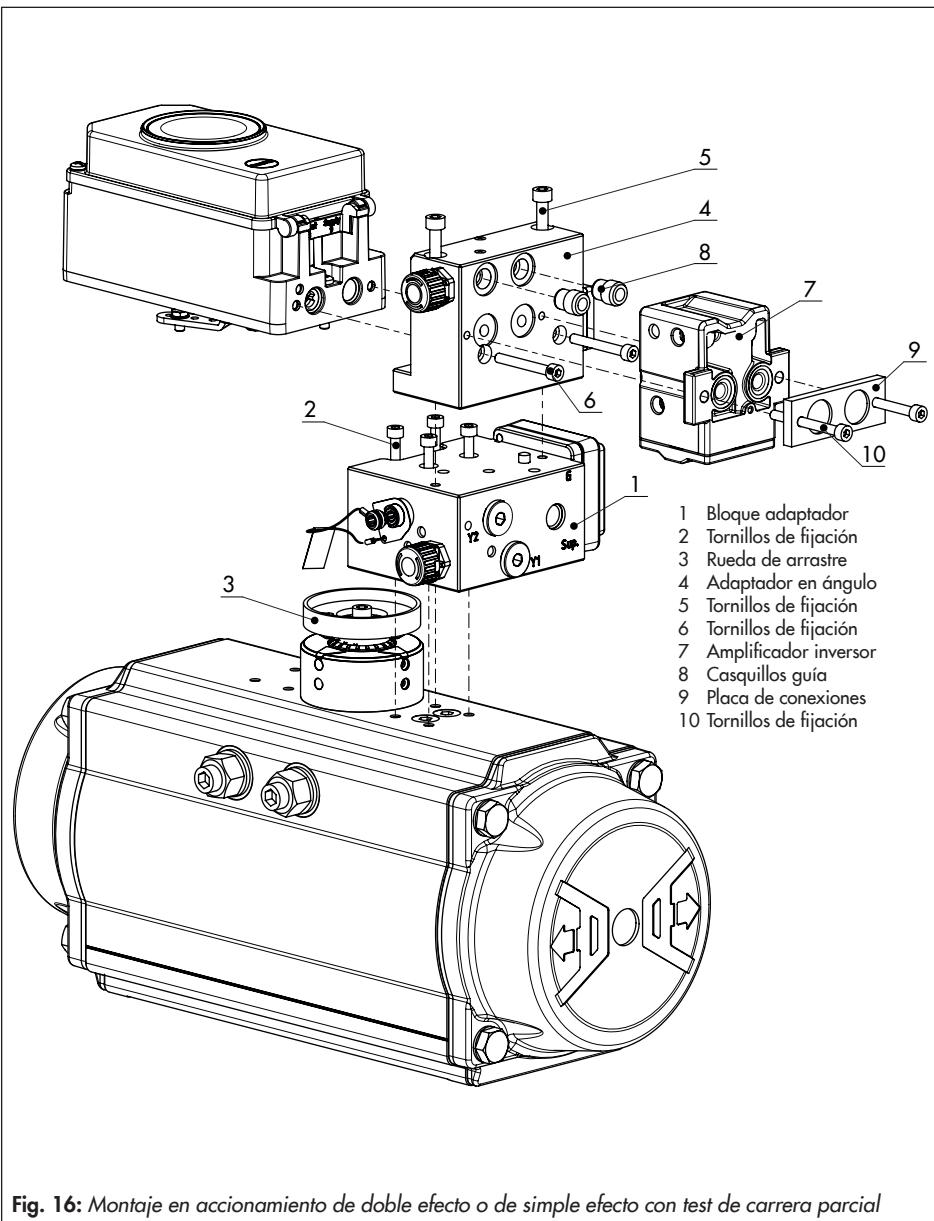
Montaje en accionamiento de doble efecto o de simple efecto con test de carrera parcial
